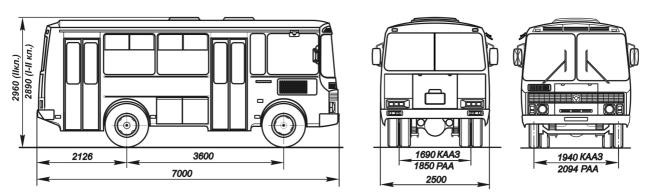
Габаритные размеры автобуса ПАЗ-32054-07
